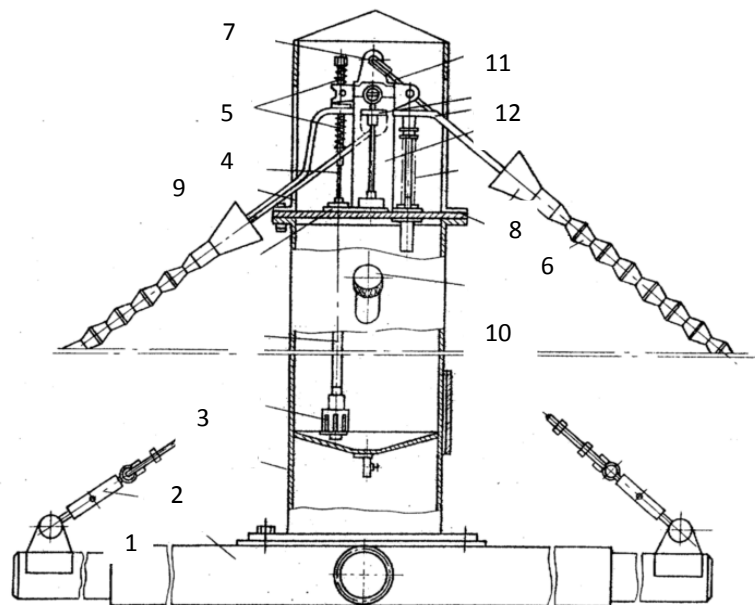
Универсальное устройство для санитарной очистки кожного покрова.
